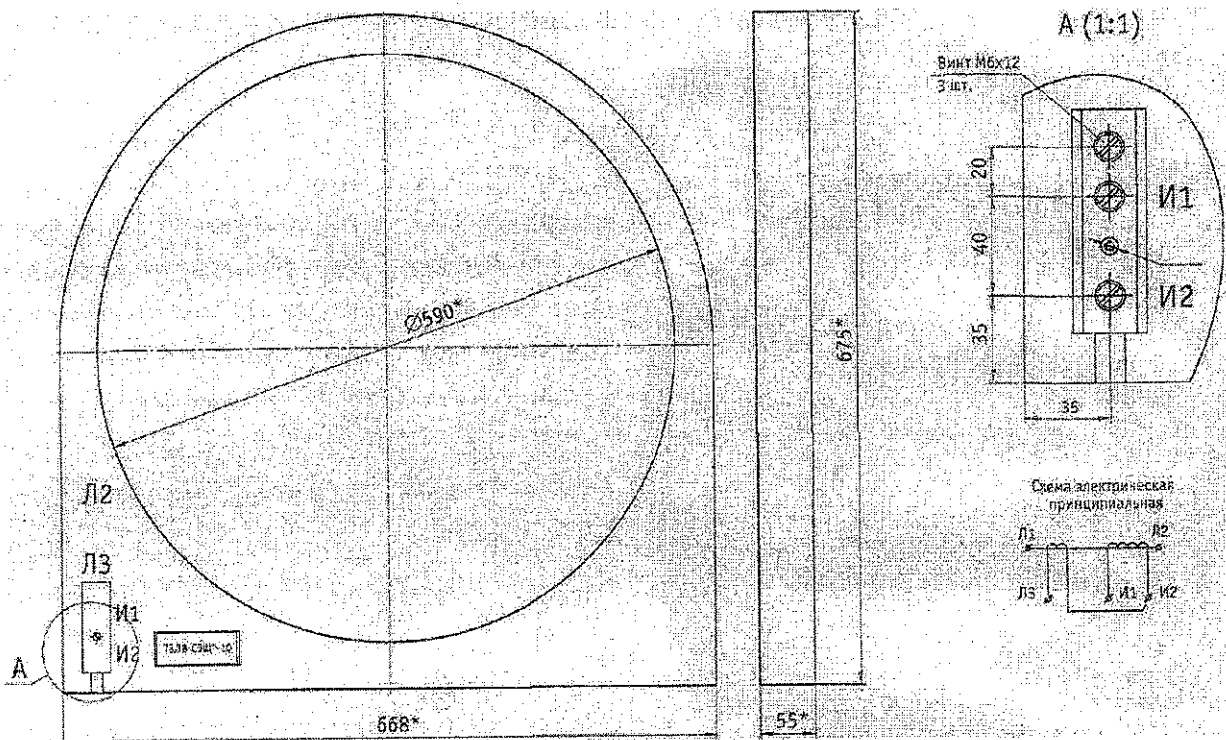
Габаритные, установочные размеры датчика тока ТЗЛВ-СЭЦ®
